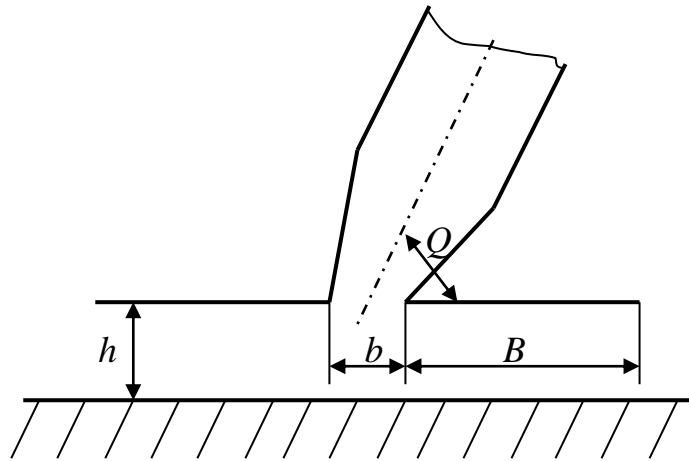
Форма насадка коллекторного типа, предложенного для сбора древесной пыли
